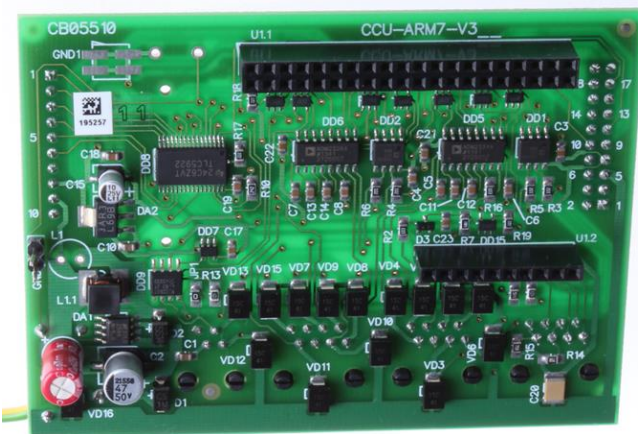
Внешний вид базового модуля контроллера «Синком-Д»
